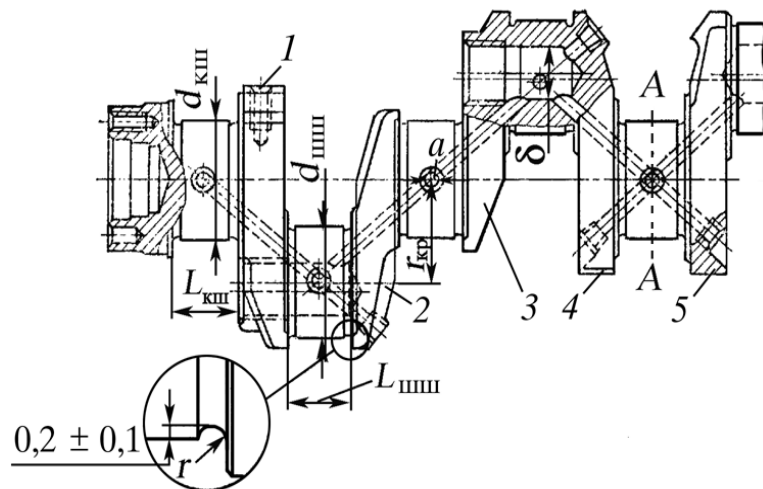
Чертеж коленчатого вала четырехтактного дизеля:
